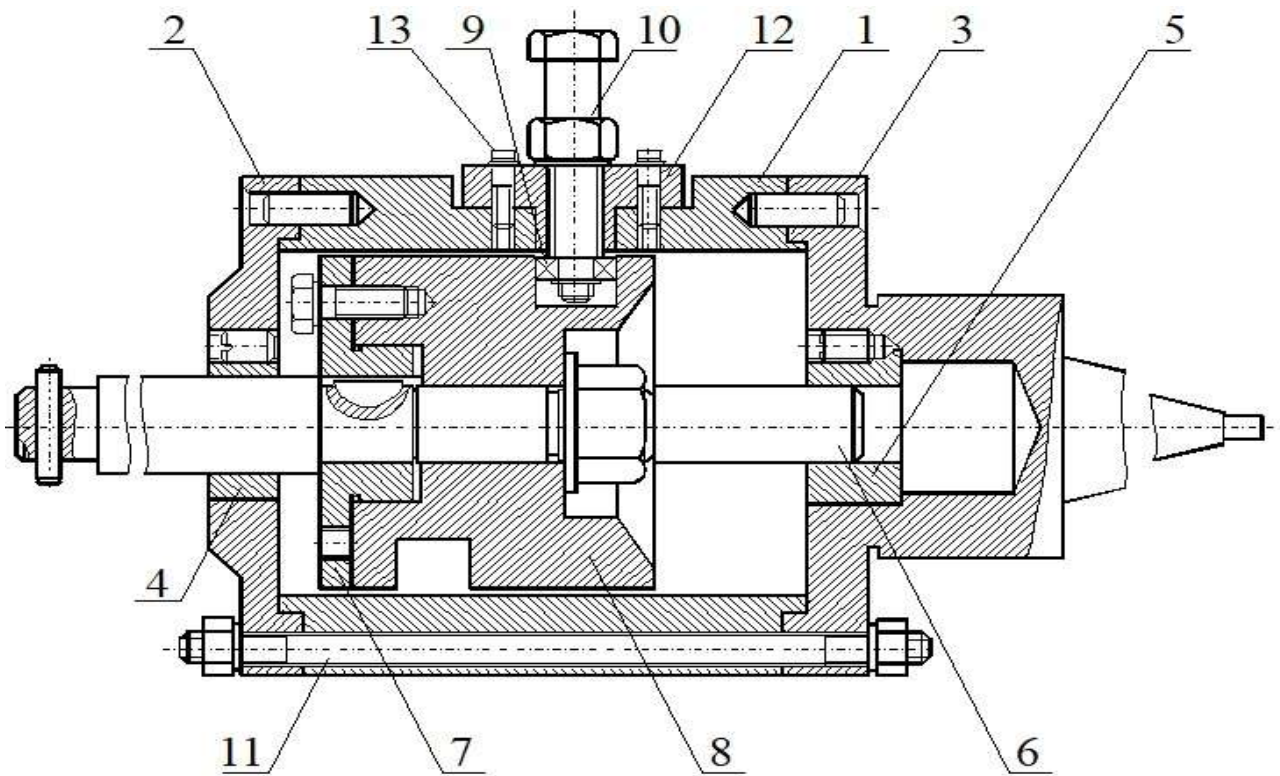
Осциляційний вузол: 1 – корпус; 2 – кришка передня; 3 – кришка задня; 4, 5 - втулка напрямна; 6 – вал; 7 – маточина; 8 – копір змінний; 9 – упор; 10 – гвинт; 11 – шпилька; 12 – втулка знімна; 13 – болт.
